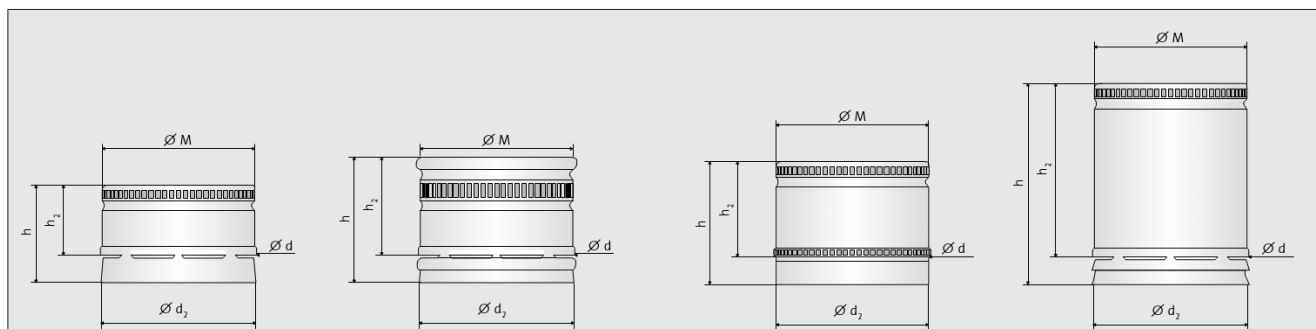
Disegni tecnici di capsule a vite in alluminio
